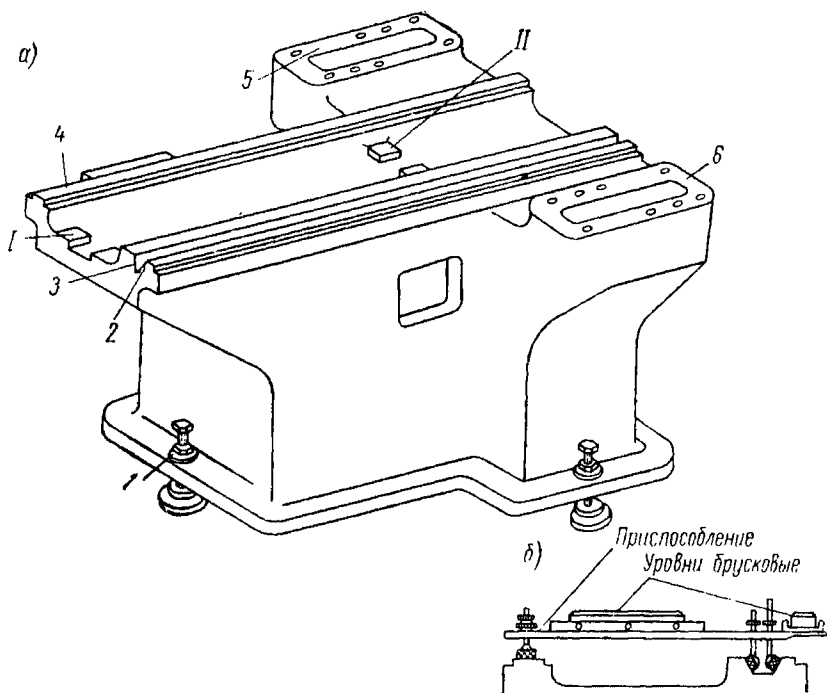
Станина станка КР-450; а — общий вид; б — схема проверки направляющих
